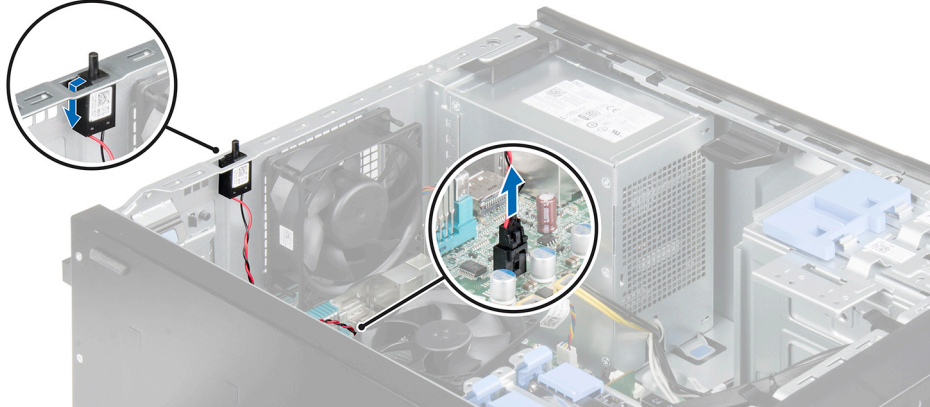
Entfernen des Gehäuseeingriffschalters
